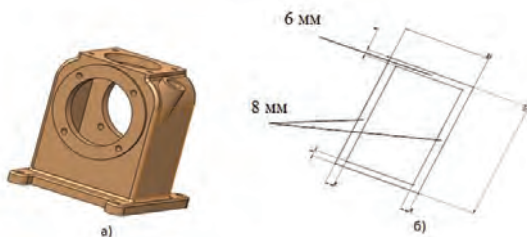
а) корпус вакуумного насоса, б) эскиз заготовки корпуса.
